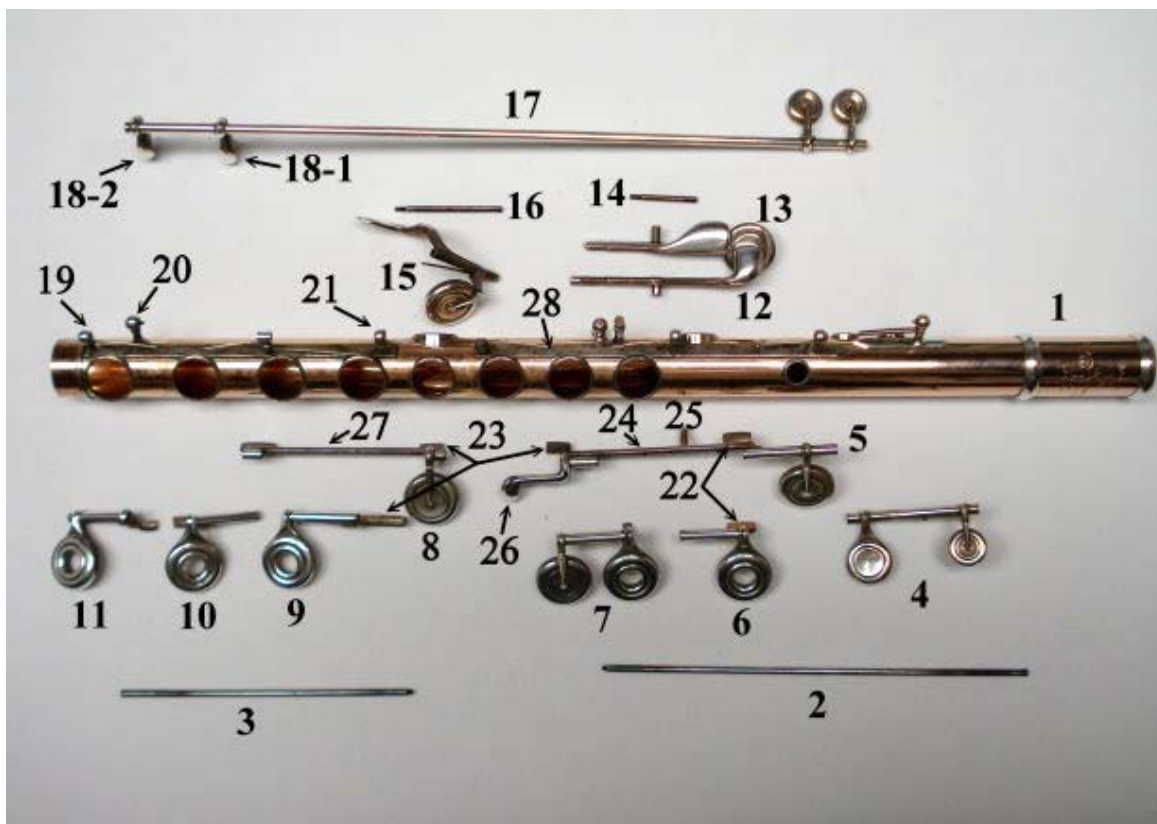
Устройство основного корпуса флейты Бреггера
